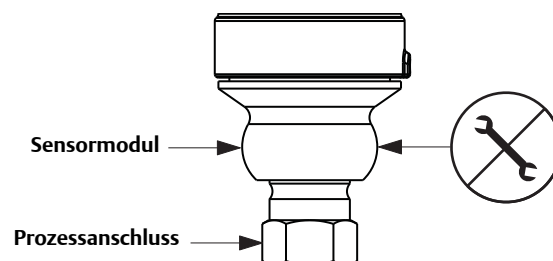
Niederdruckanschluss des In-Line Überdruck-Messumformers
